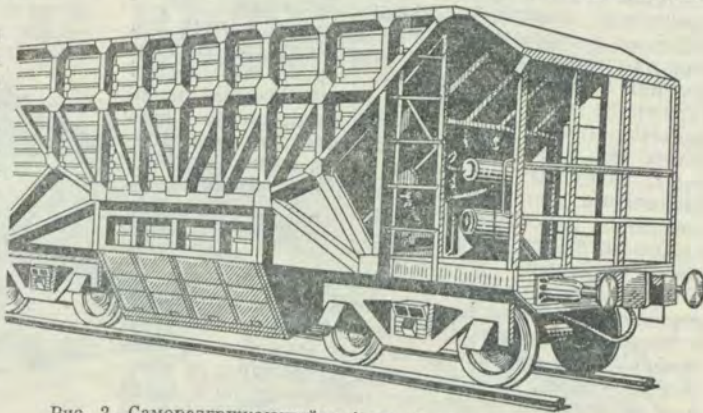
Саморазгружающийся 4-осный вагон для перевозки горячего агломерата.
